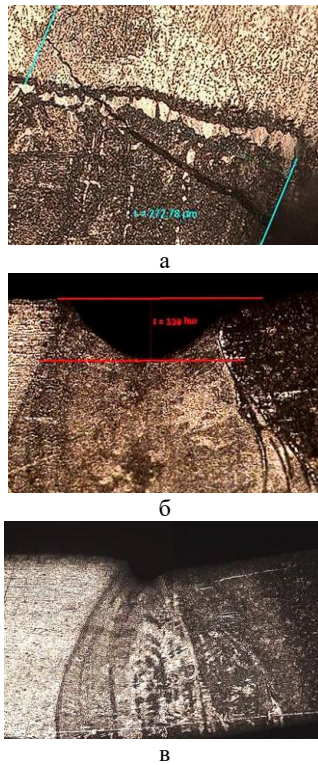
Дефекти деяких зварних з'єднань зразків:
